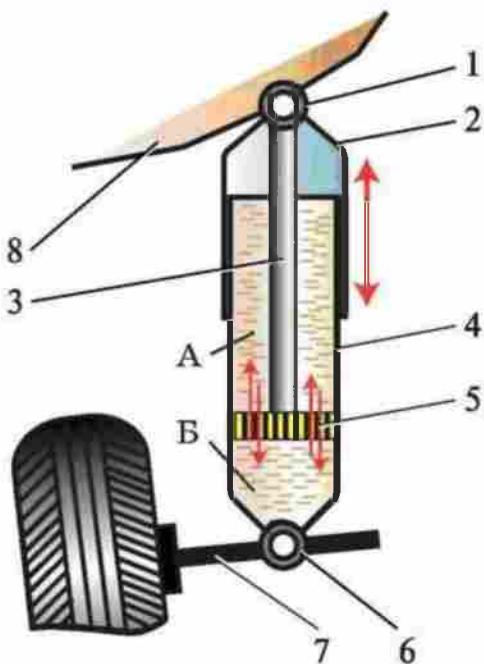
Схема амортизатора: 1 - верхняя проушина; 2 - защитный кожух; 3 - шток; 4 - цилиндр; 5 - поршень с клапанами сжатия и "отбоя"; 6 - нижняя проушина; 7 - рычаг подвески; 8 - кузов автомобиля.
